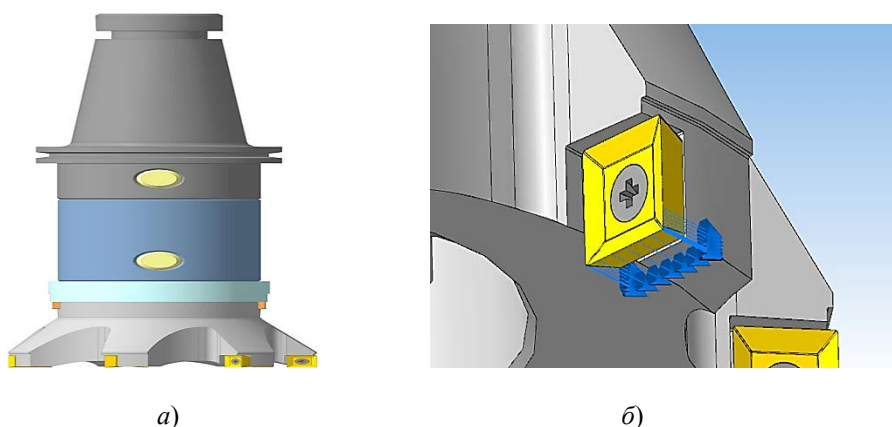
3D-модель торцевой фрезы F90SD D125-40-CP12 (а) и схема воздействия силы P_z на режущую пластину (б)
